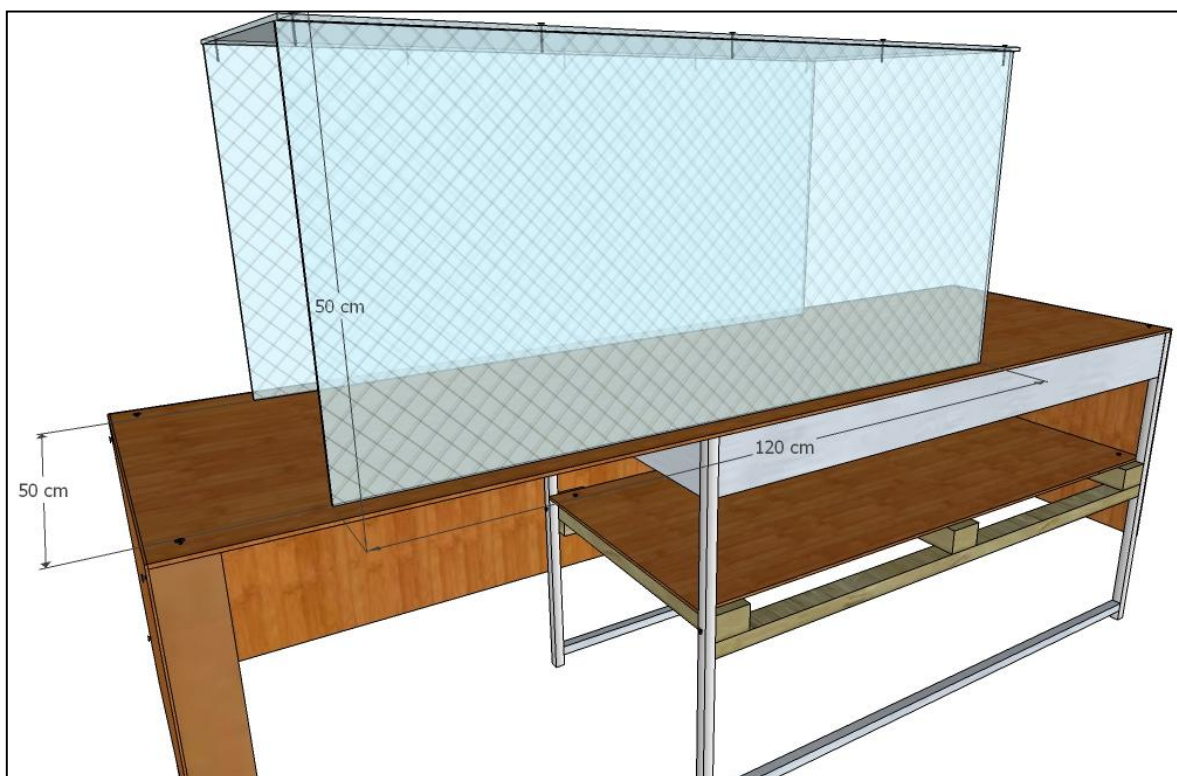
Diseño mecánico del cuerpo del túnel de viento.
